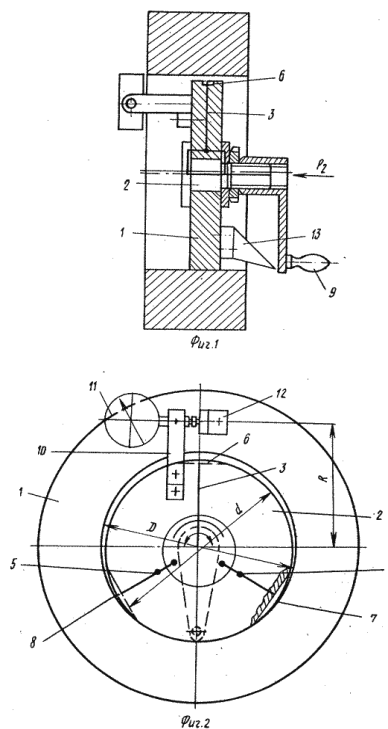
Пристрій для вимірювання внутрішніх діаметрів деталей
